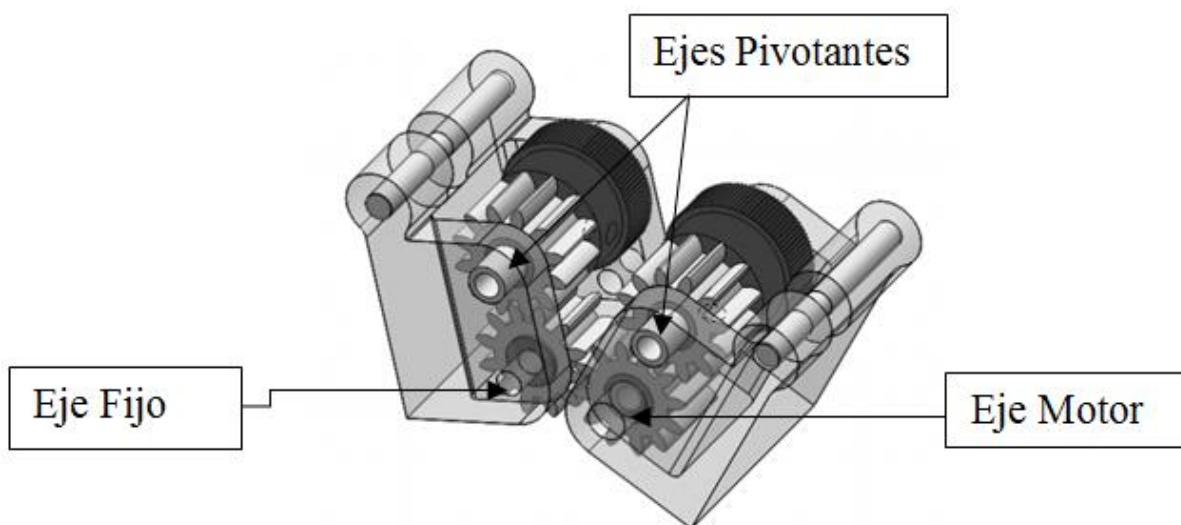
Ejes fijos y móviles del extrusor de engranajes pivotantes (Versión 02)
